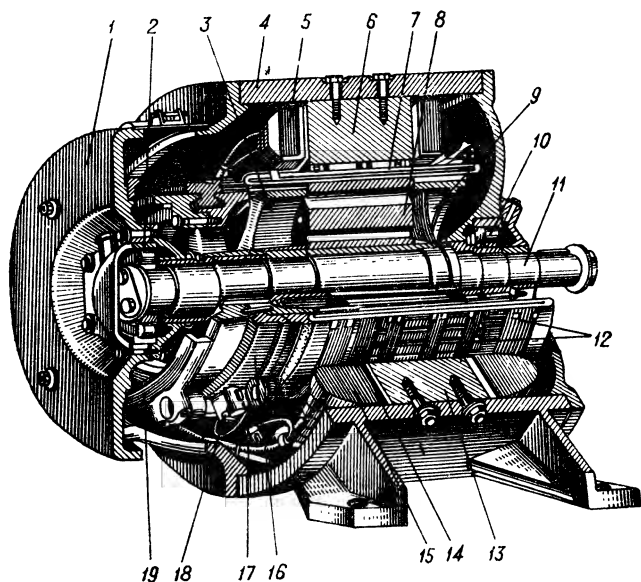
Электродвигатель НБ-431А компрессора КТ-6
